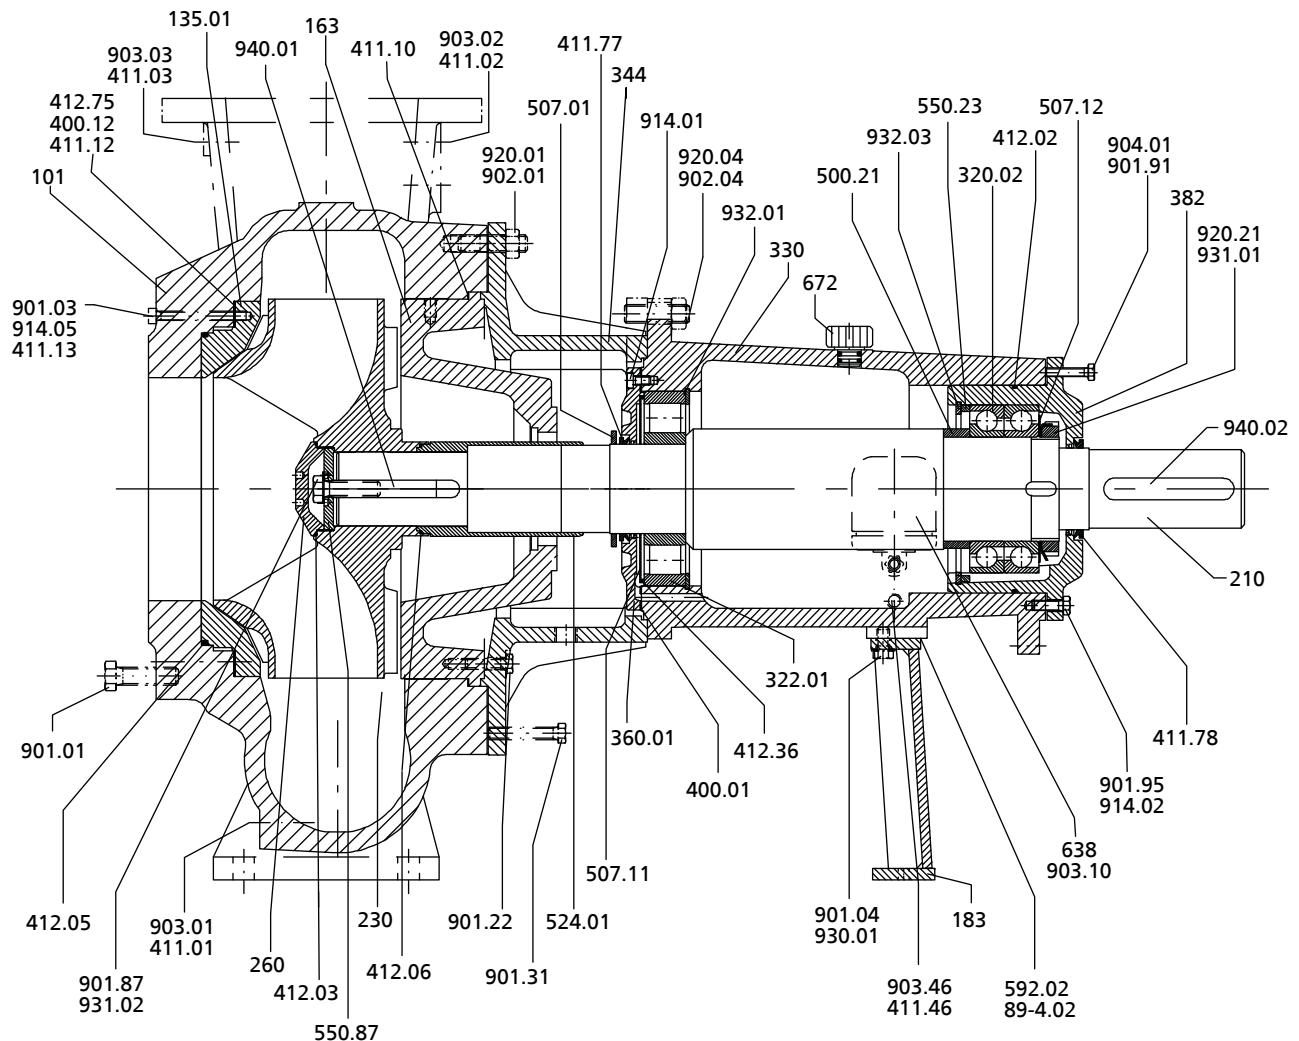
Gesamtzeichnung Pumpe mit Lagerträger P08sx bis P12sx
